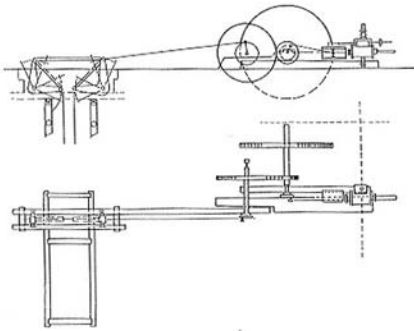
Seitenansicht und Draufsicht der Dampfmaschine für den Pumpenantrieb des Kanekuhler Schachtes mit Vorgelege und Kunstdreiecken über dem Schacht, Zeichnung aus der Sammlung Heinrich Stöcker
